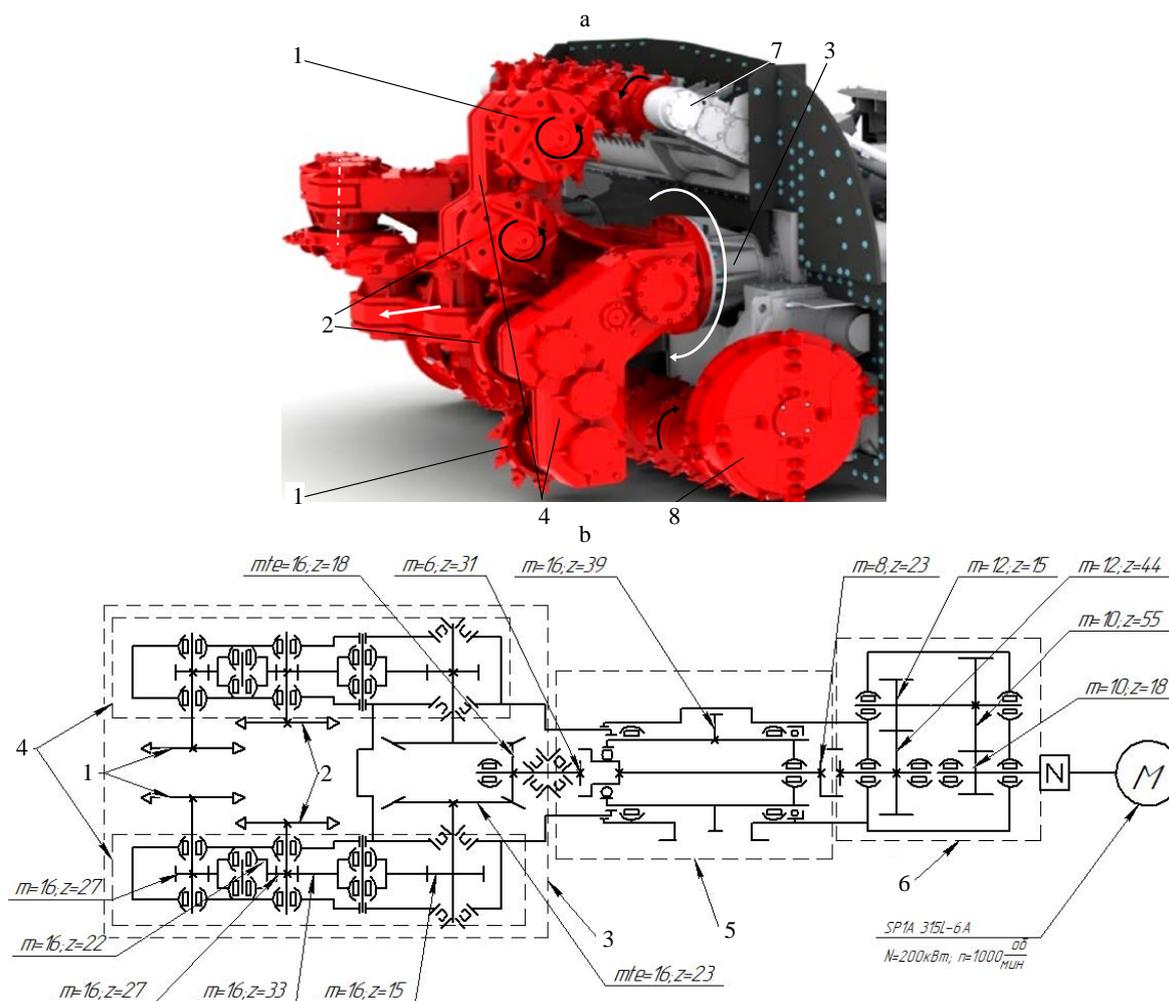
Общий вид режущих органов горного комбайна «Универсал 600» (а) и кинематическая схема привода исполнительного органа (б): 1, 2 – наружный и внутренний режущие диски; 3 – зубчатый редуктор привода вращения режущих дисков с коническими зубчатыми колесами z18 и z23; 4 – рукояти зубчатого редуктора привода вращения режущих дисков, в которых размещена цепь прямозубых шестерен z27, z22, z33 и z15; 5 – корпус редуктора привода вращения исполнительного органа с приводной шестерней z39; 6 – корпус входного зубчатого редуктора с z44, z15, z55 и z18; 7 – отбойное устройство; 8 – бермовый орган
